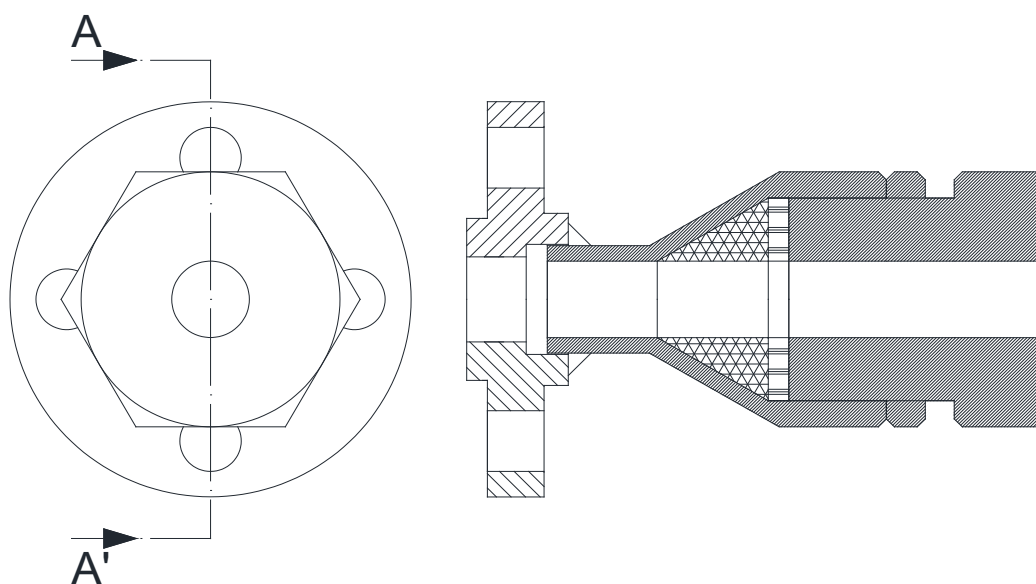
primer modelo de conector retráctil soldado sobre brida 1", a la izquierda vista superior a la derecha corte A-A'.
